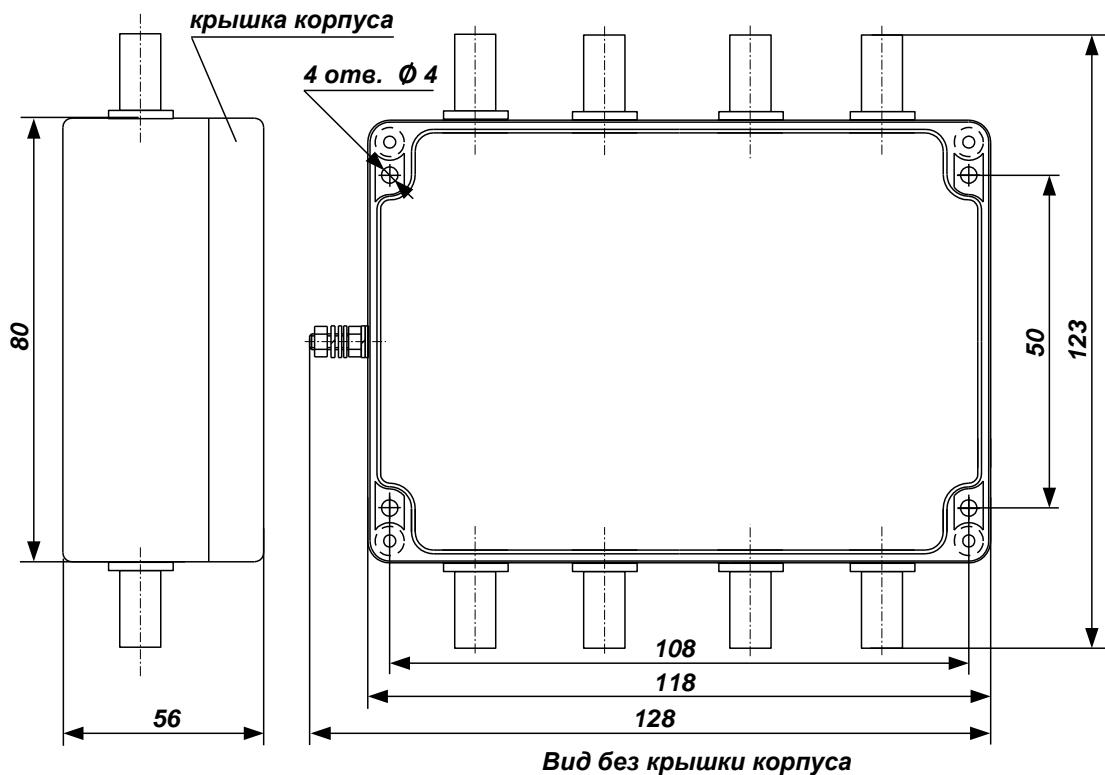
Габаритные и присоединительные размеры БЗВВ-04
